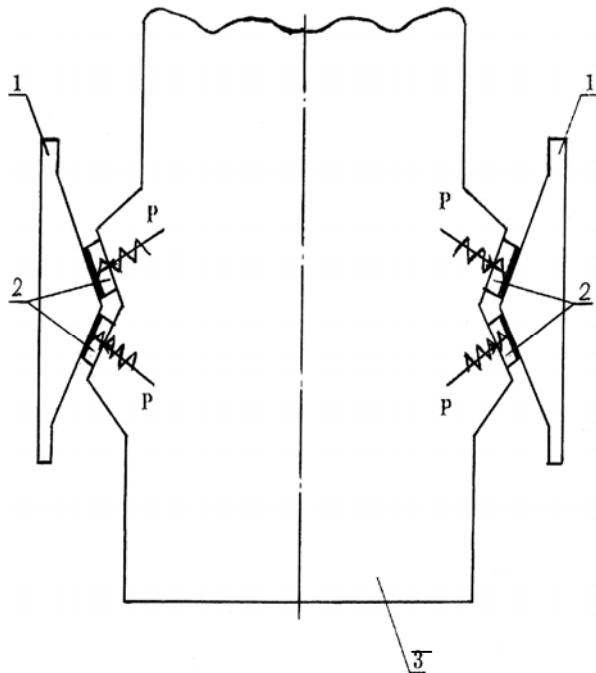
Связи между надрессорной балкой и боковинами (вид сверху):
